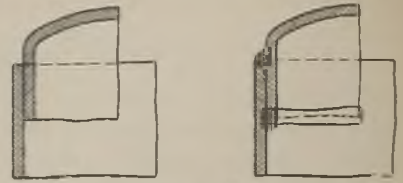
Anschweißen eines Keilbodens, mit Überlappung — außen und innen verschweißt (doppelte Schweißnaht, hochbeansprucht).
